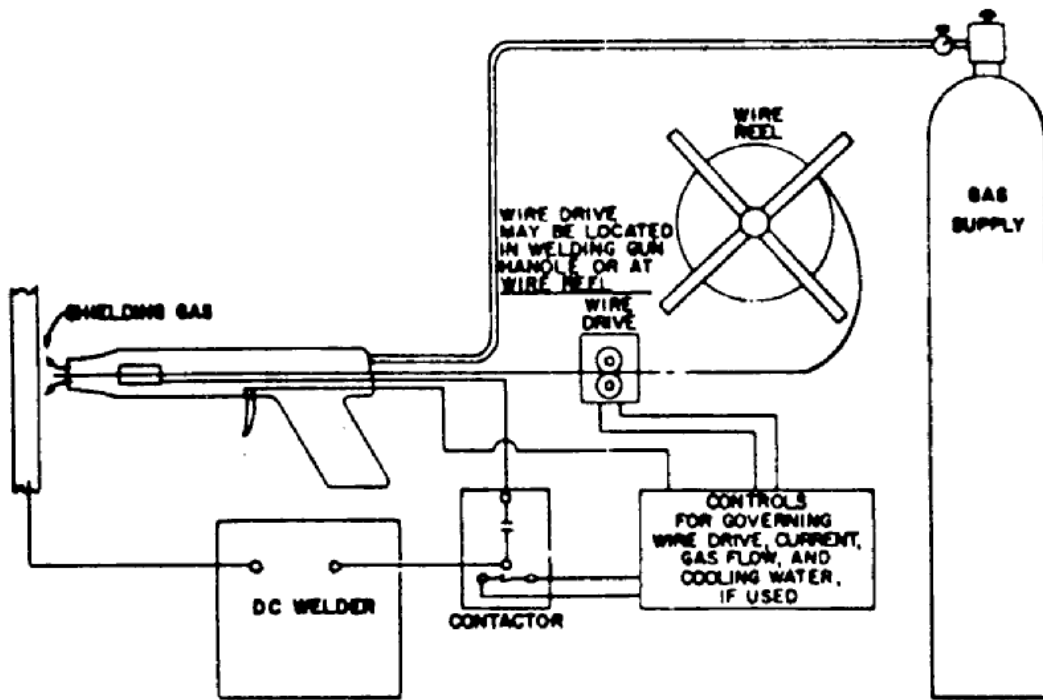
Soldadura MIG (gás inerte) ou MAG (CO₂)
